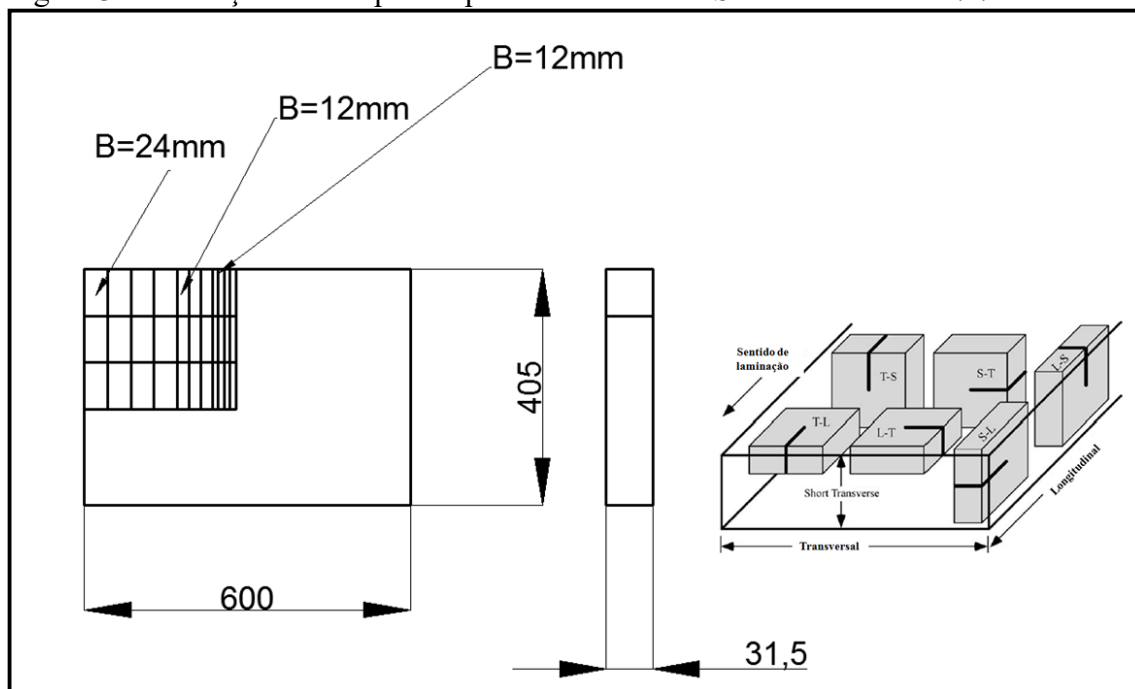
Geometrias obtidas para ensaio. Dimensões em mm
